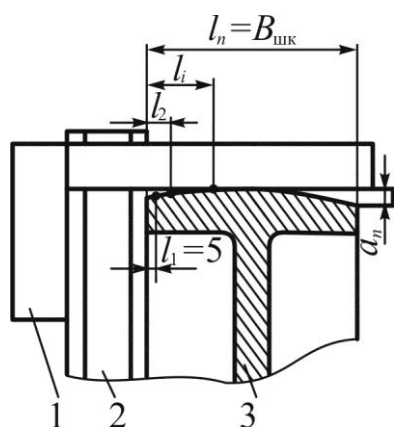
Контроль формы рабочих поверхностей шкивов ленточнопильного станка:
